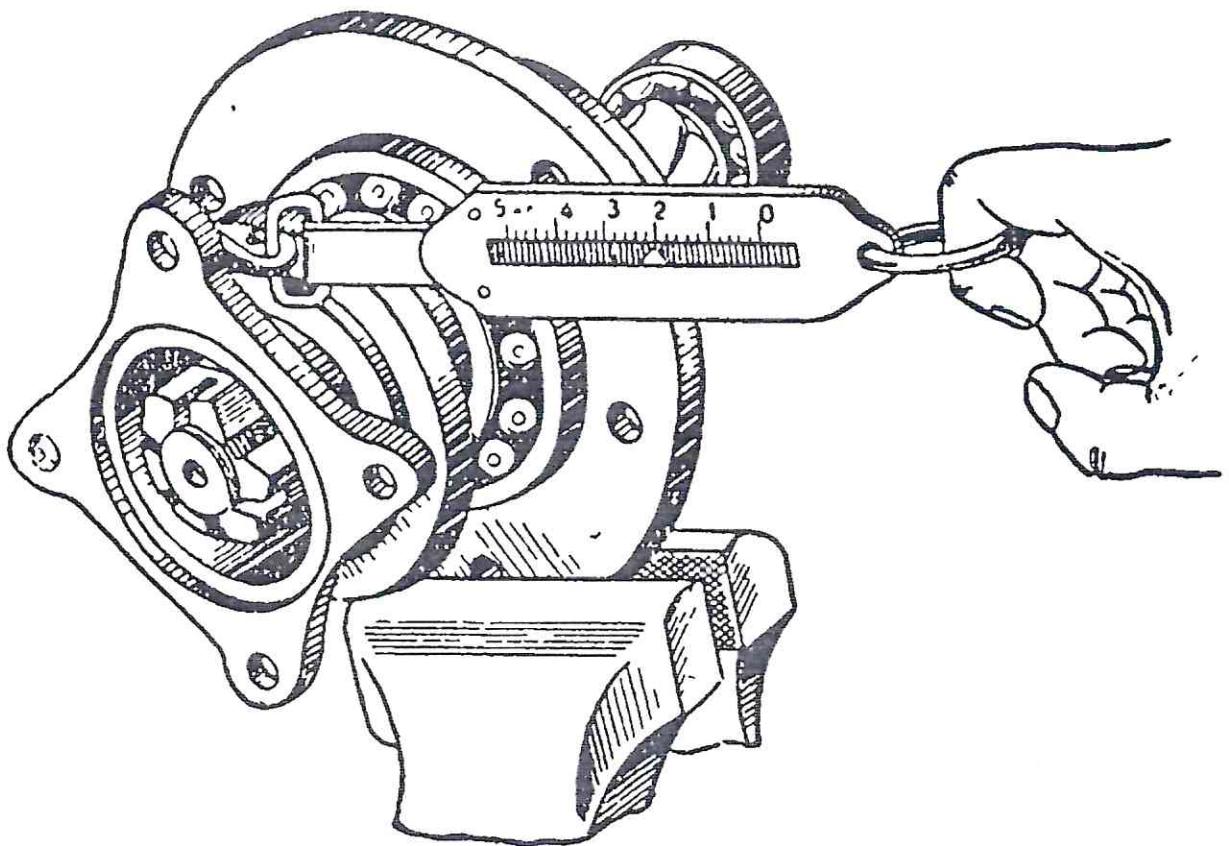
Проверка затяжки подшипников находился в пределах
